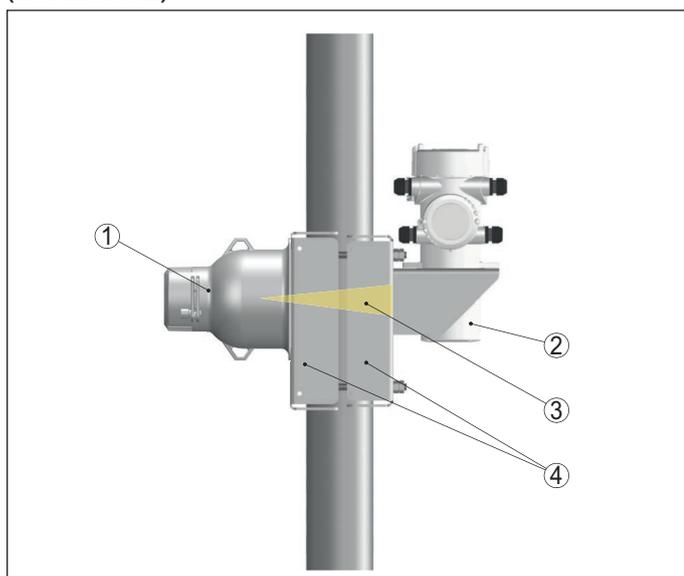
Dispositivo di fissaggio per il montaggio su tubi da 50 ... 220 mm (1.97 ... 8.66 in) con inclinazione di irraggiamento di 30°
